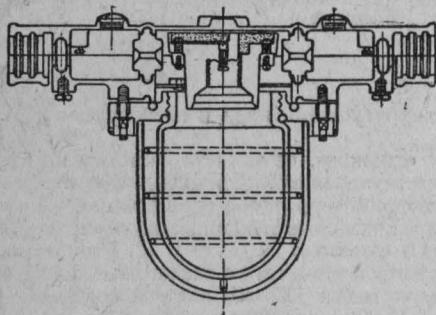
Разрез через арматуру для лампочки накаливания со штуцерами для кабеля с бумажной изоляцией.
